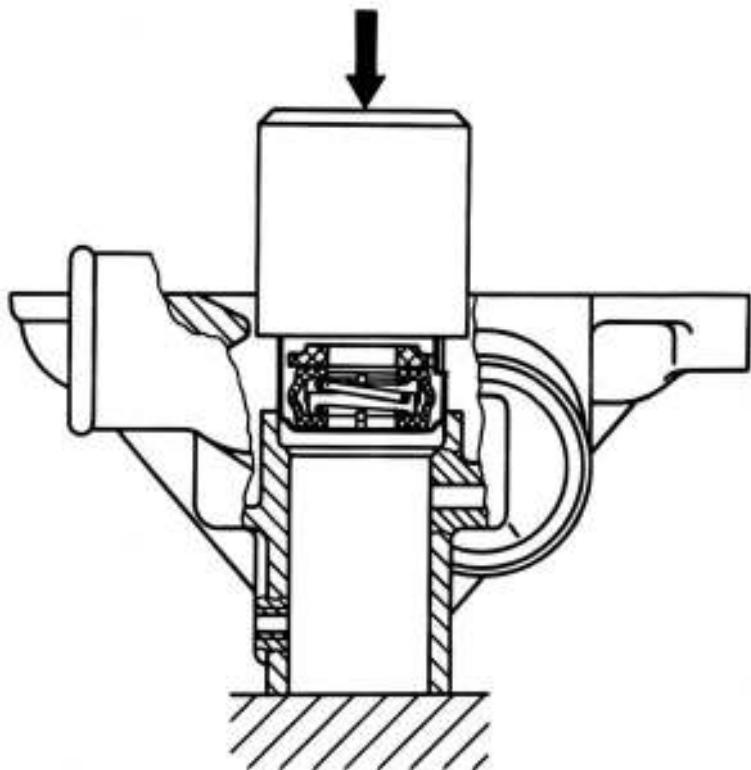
Выпрессовка подшипника с валиком насоса
